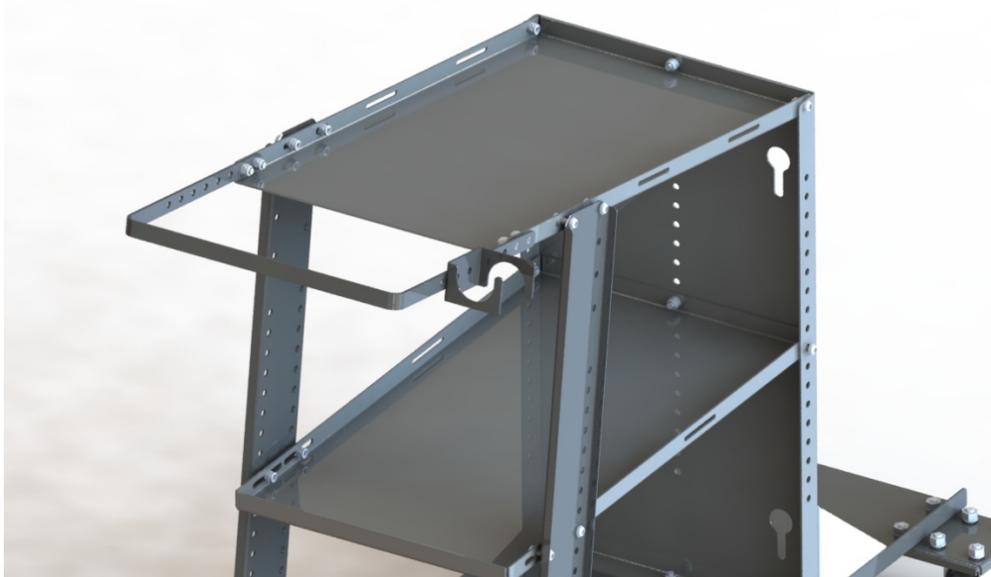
Кронштейн горелки для сварочных полуавтоматов.
